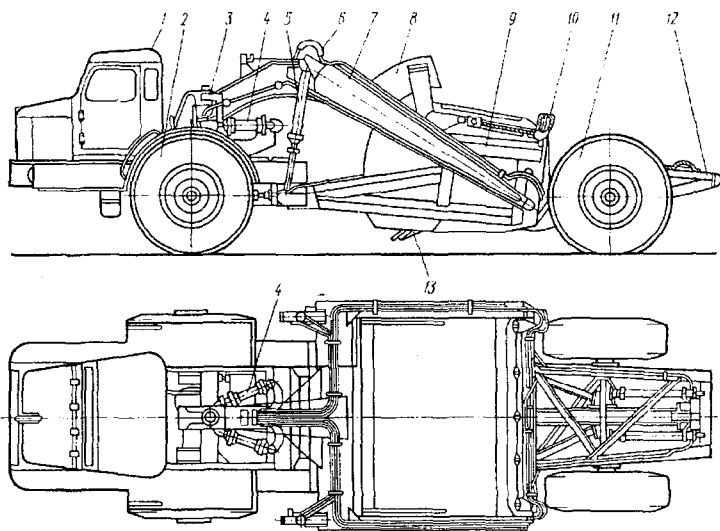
Общий вид скрепера: 1 – кабина; 2 – колесо; 3 – седельно-цепное устройство; 4 – гидроцилиндры поворота; 5 – гидроцилиндры подъема ковша; 6 – поперечная балка; 7 – упряжные тяги; 8 – заслонка; 9 – ковш; 10 – задняя стенка; 11 – заднее колесо; 12 – задняя рама; 13 – нож.
